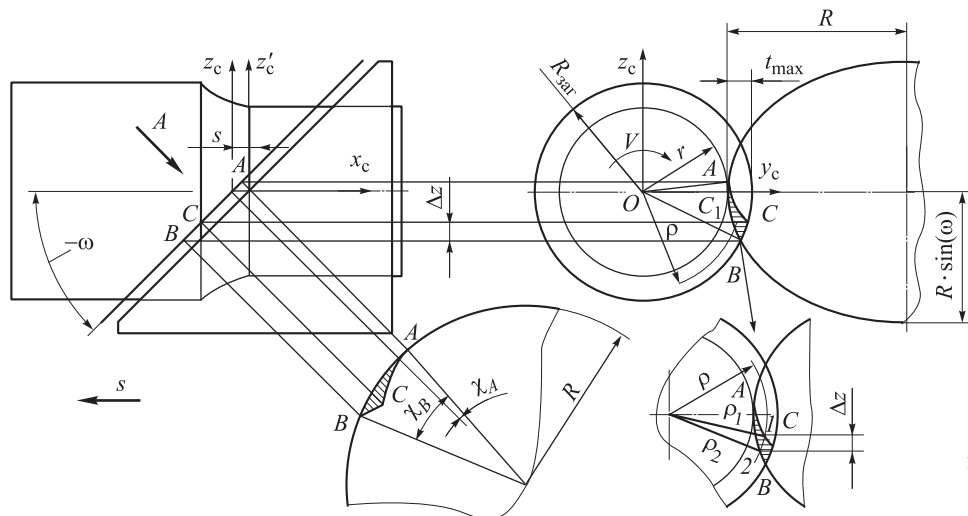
Схема косоугольного точения безвершинным резцом с радиусной задней поверхностью [6]
